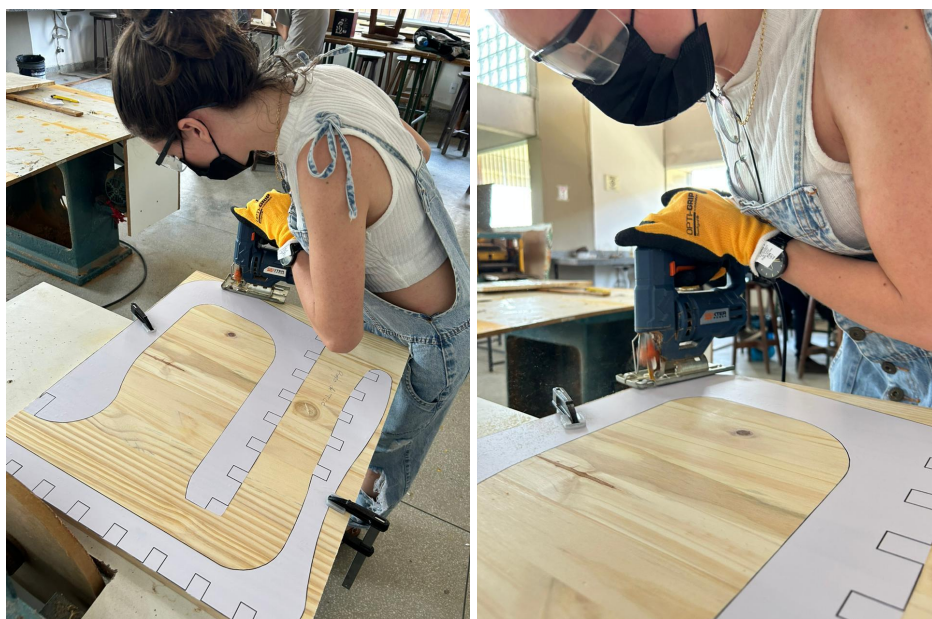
e 80 - Aplicação do adesivo plotado na madeira.
